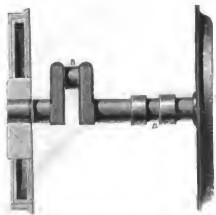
Axe mit Rädern u. Krummzapfen; fen.
